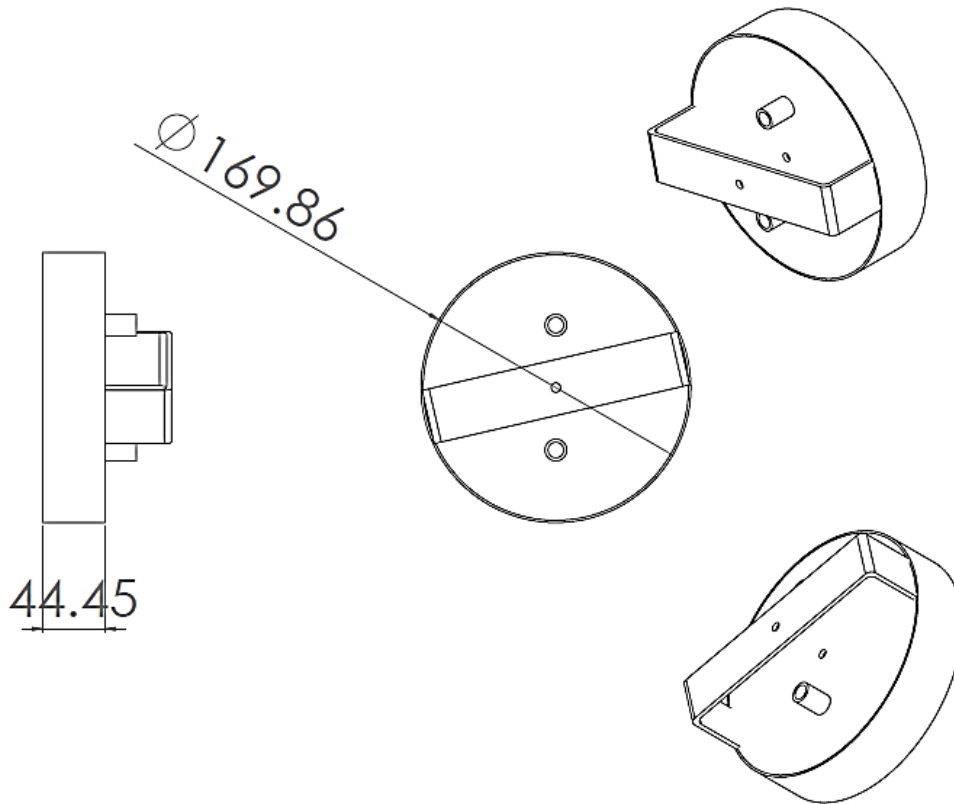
Dibujos técnicos de la tapa cilíndrica superior.
